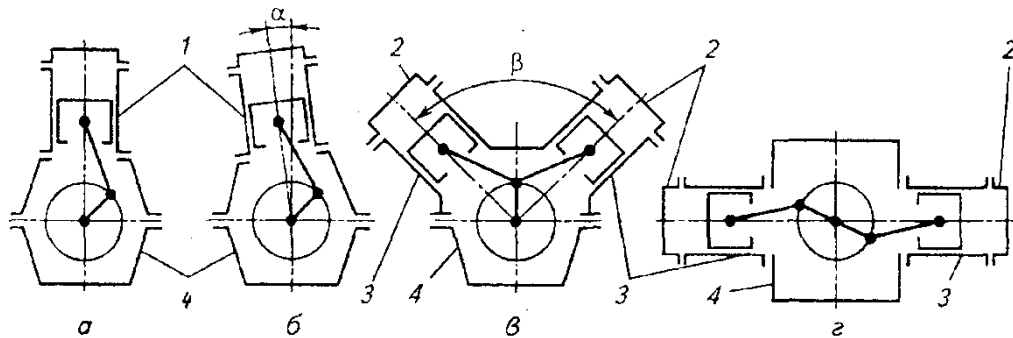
Схемы расположения цилиндров двигателя: а — однорядного; б — однорядного с наклоном к вертикали; в — V-образного; г — с противоположно лежащими цилиндрами; 1 — цилиндр; 2 — головка блока; 3 — блок цилиндров; 4 — поддон.
